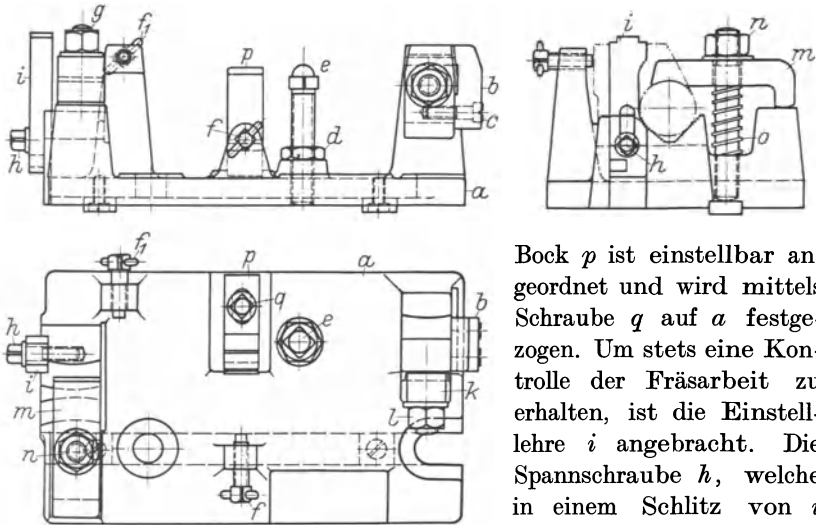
Fräsvorrichtung für Vorschubschieber.
